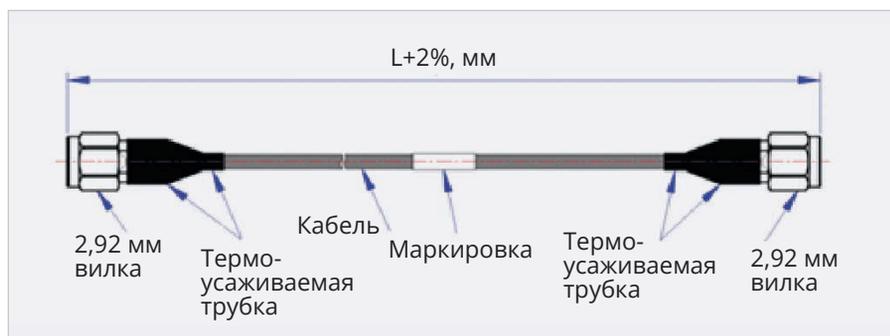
Кабельная сборка с соединителями 2.92 мм вилка – 2.92 мм вилка
